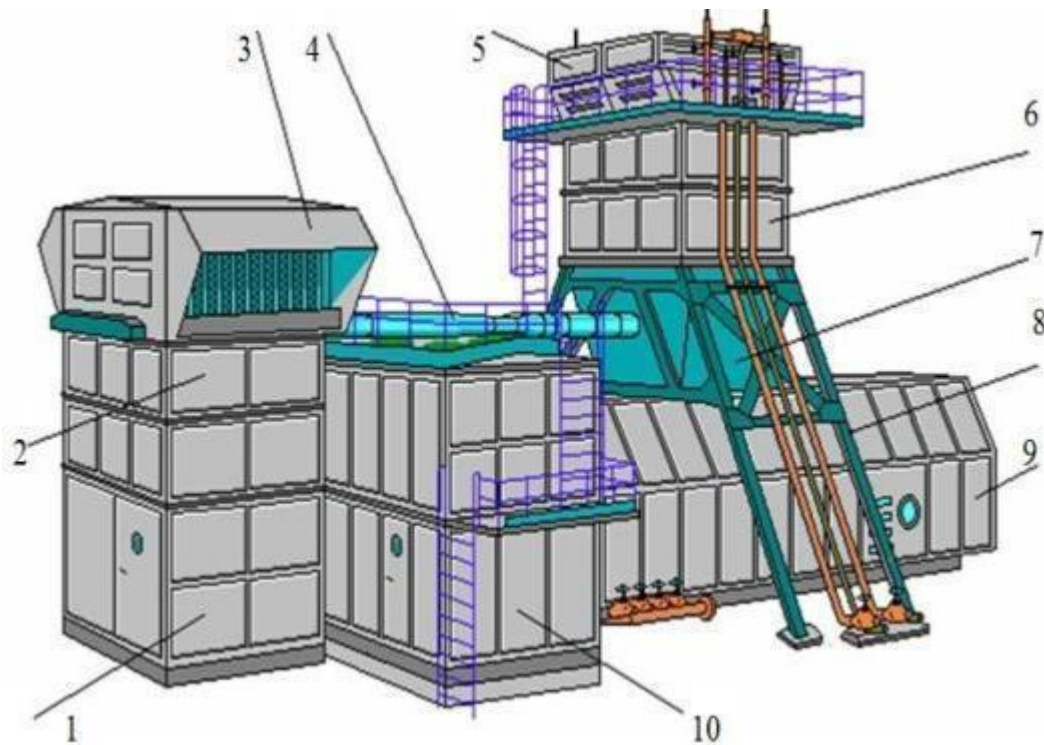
Газоперекачувальний агрегат: 1 – камера всмоктування; 2 – всмоктувальні шумоглушники; 3 – повітроочисний пристрій; 4 – система підігріву циклового повітря; 5 – утилізатор; 6 – шумоглушники вихлопу; 7 – дифузор; 8 – опора вихлопної частини; 9 – турбоблок; 10 – блок маслоагрегатів
